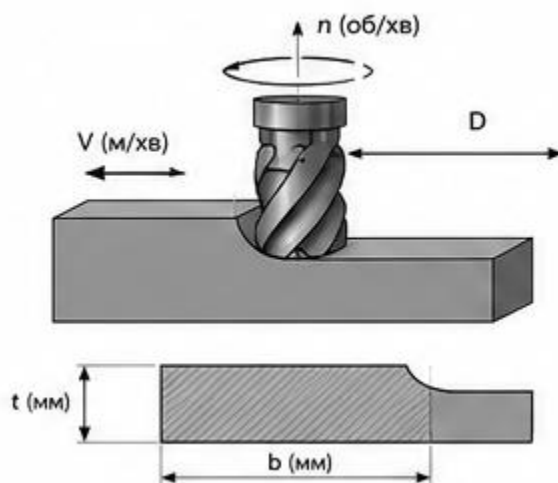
Схема визначення швидкості різання при фрезеруванні[11]
